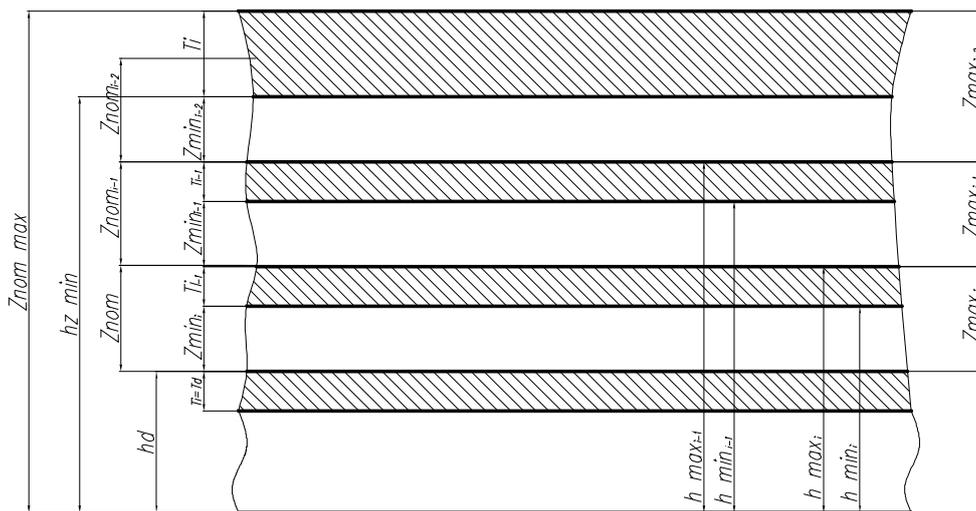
Схема связей между межпереходными размерами, припусками и допусками для охватываемых поверхностей
